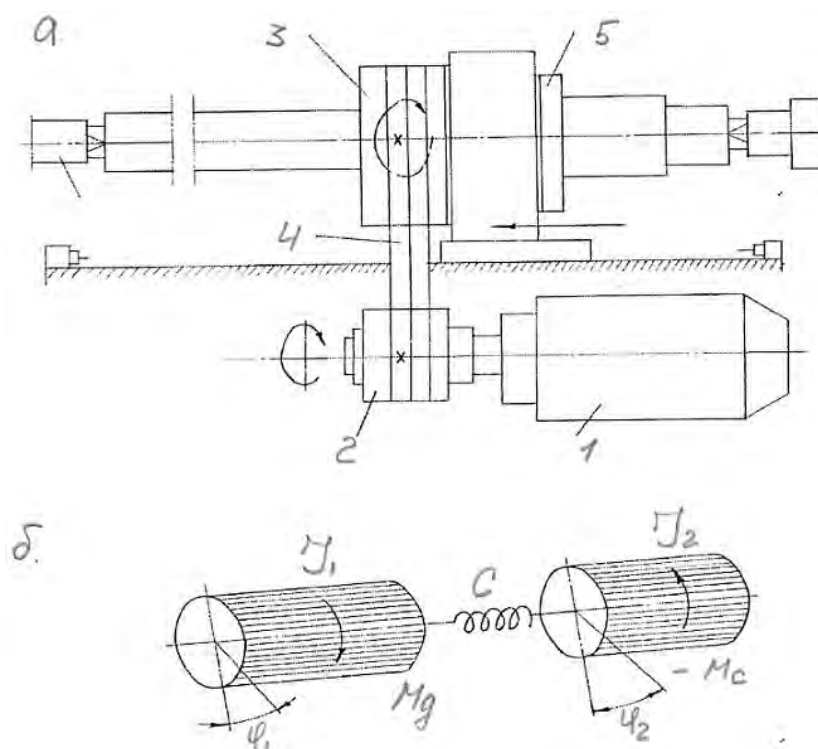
Кинематическая (а) и приведенная (б) двухмассовая схемы привода механизма резания позиционного оцилиндровочного станка
